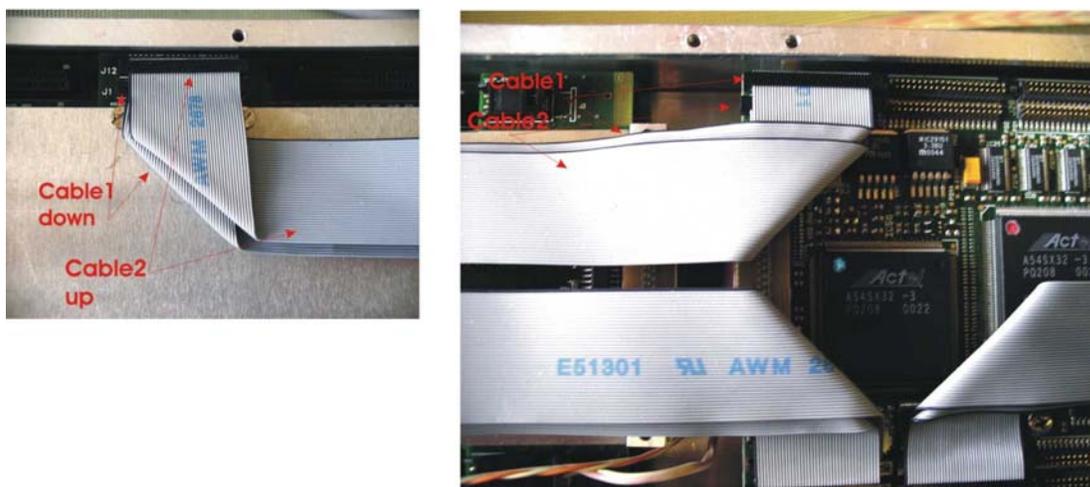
Connessioni e disposizione dei cavi di trigger: particolare.
